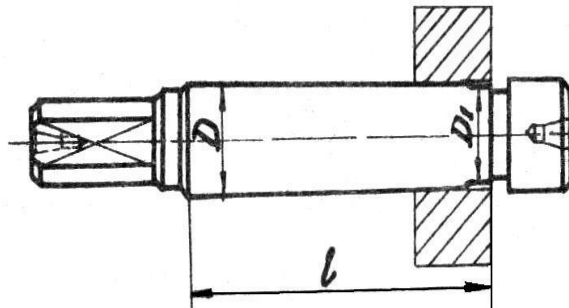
Схема установки заготовки на центрову жорстку оправку
